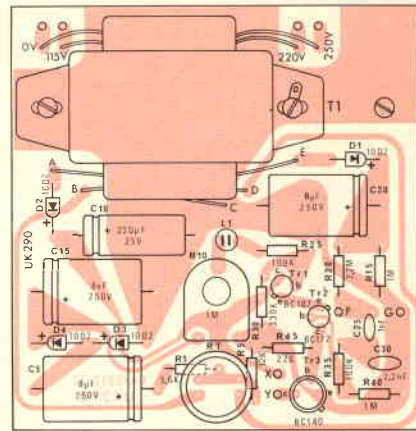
Montaggio dei componenti sul circuito stampato.
